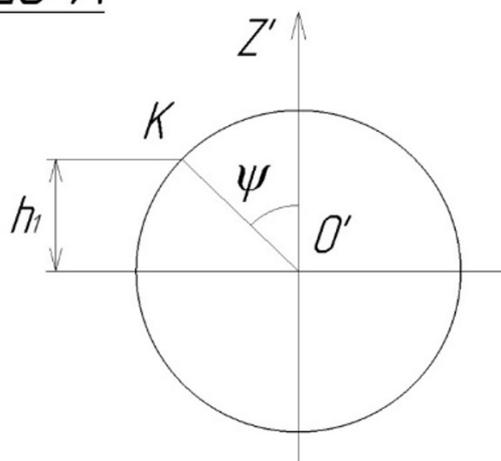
Расчетная схема расположения режущей чашки относительно обрабатываемой детали
